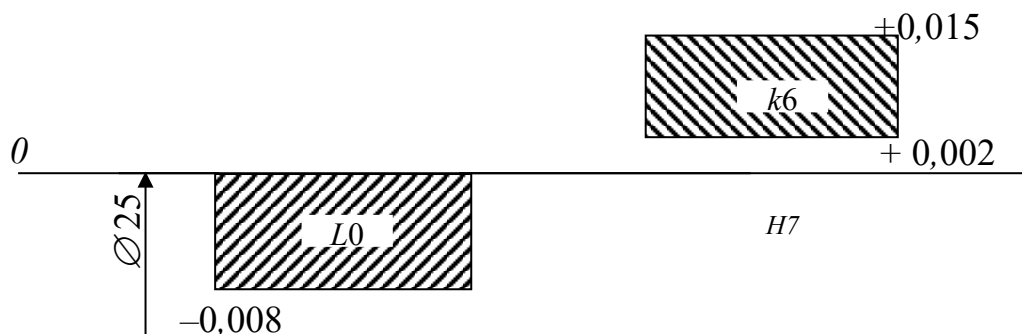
Посадка внутрішнього кільця підшипника
